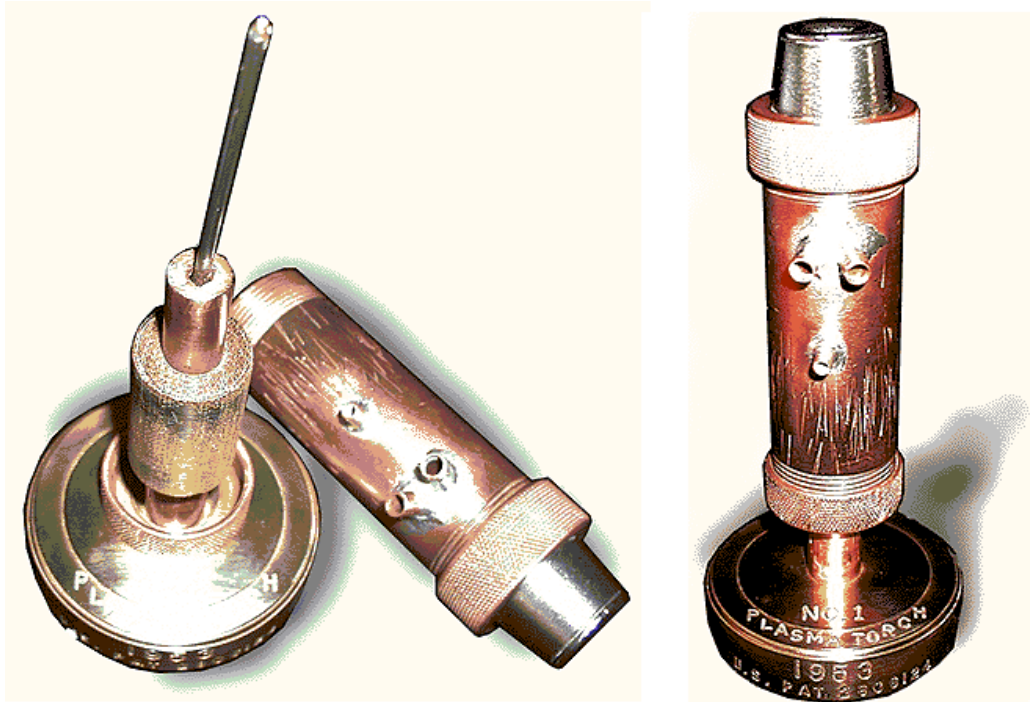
Primeira tocha plasma patenteada (*American Welding Society*, disponível em <http://www.aws.org/about/gage.html> ).
